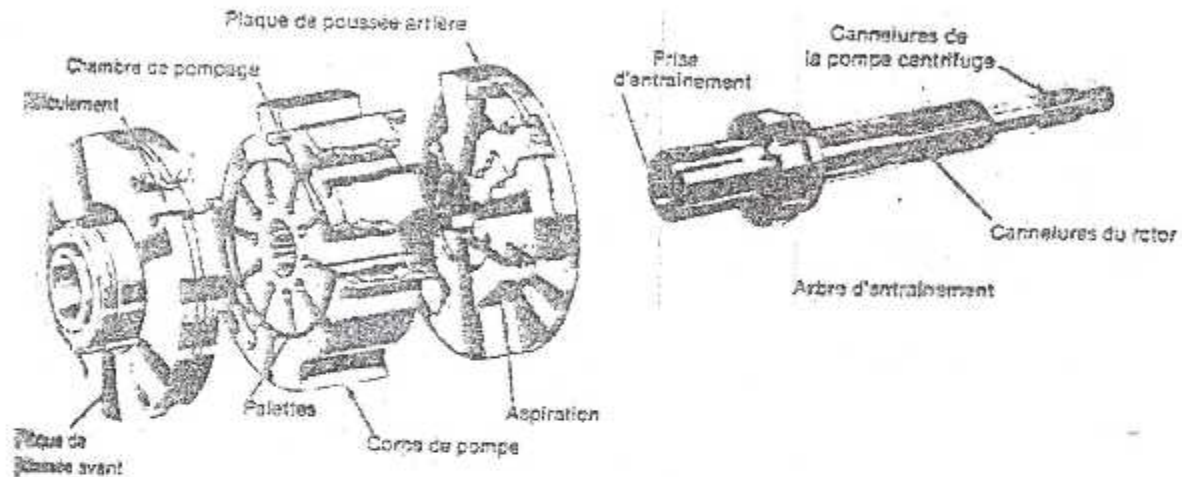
vue en éclaté de la pompe de carburant Vickers à palettes
